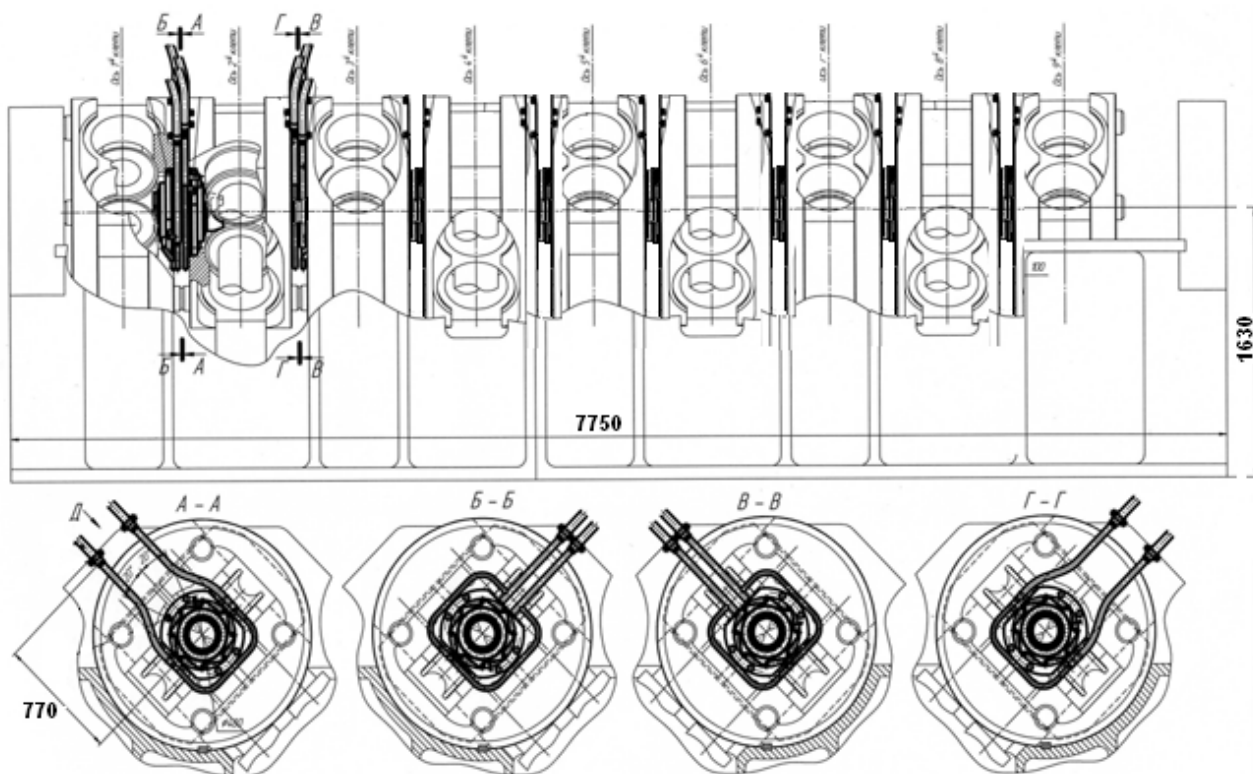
Схема установки спрейеров МКО в клетях калибровочного стана
